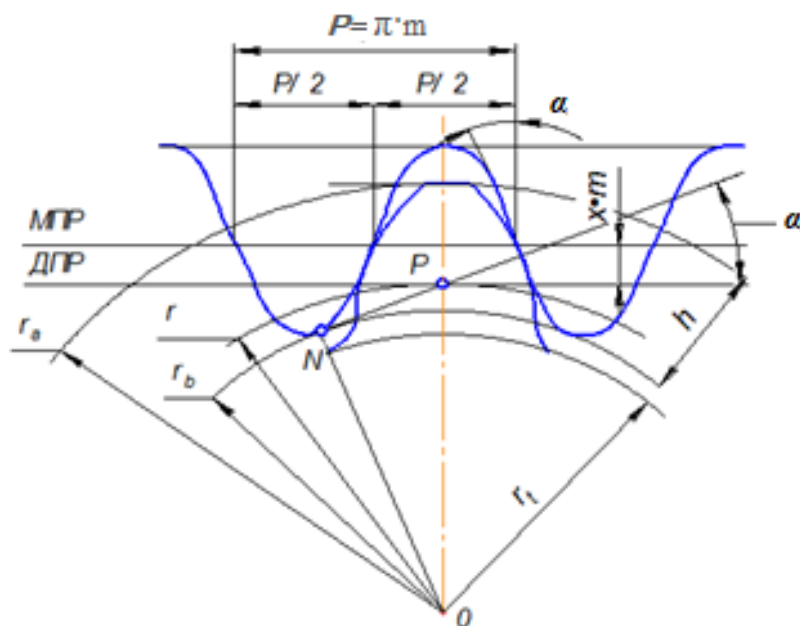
Зацепление зубчатого колеса с инструментальной рейкой
